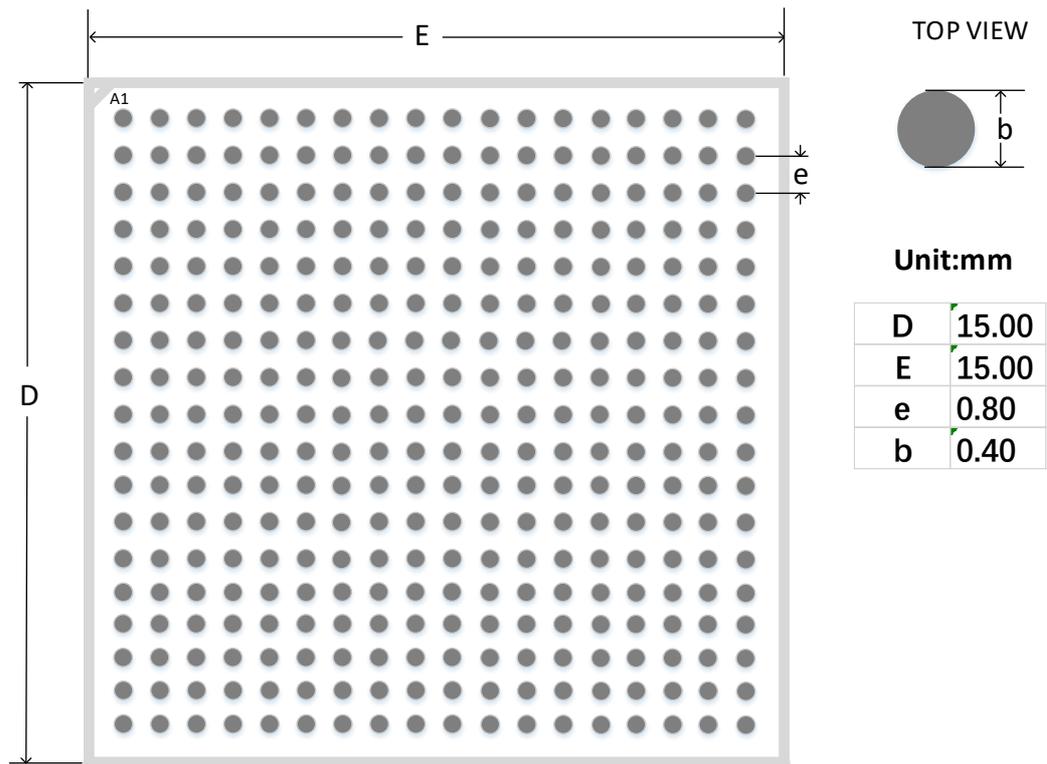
推荐 PCB Layout UG324A (GW5AT-60)
